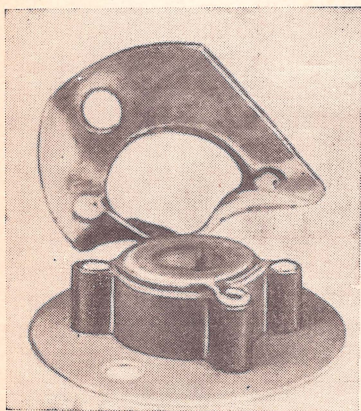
Муфта центрифуги: центральная втулка (металло-керамика, пропитанная медью) соединена с фланцами из холоднокатаной стали точечной сваркой
